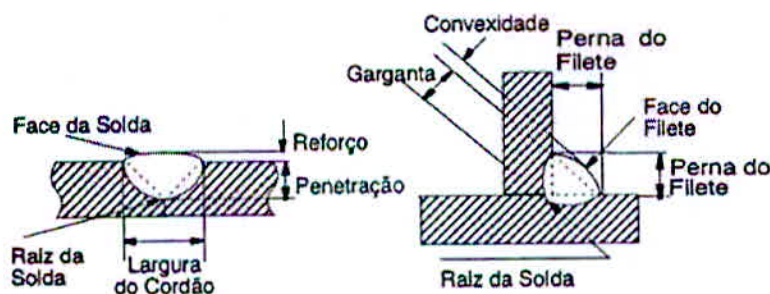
Algumas dimensões e regiões de soldas de topo e filete
